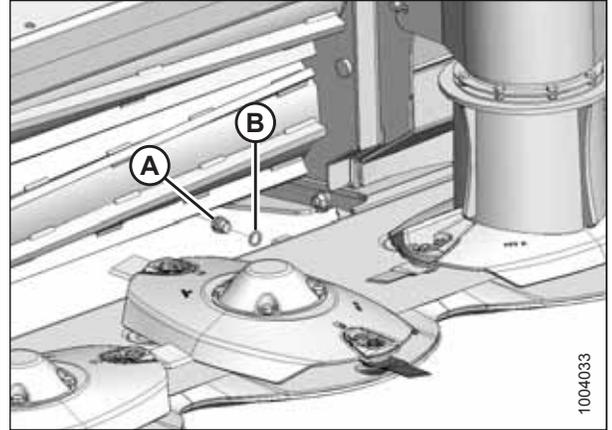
Bouchon d'inspection d'huile de barre de coupe
